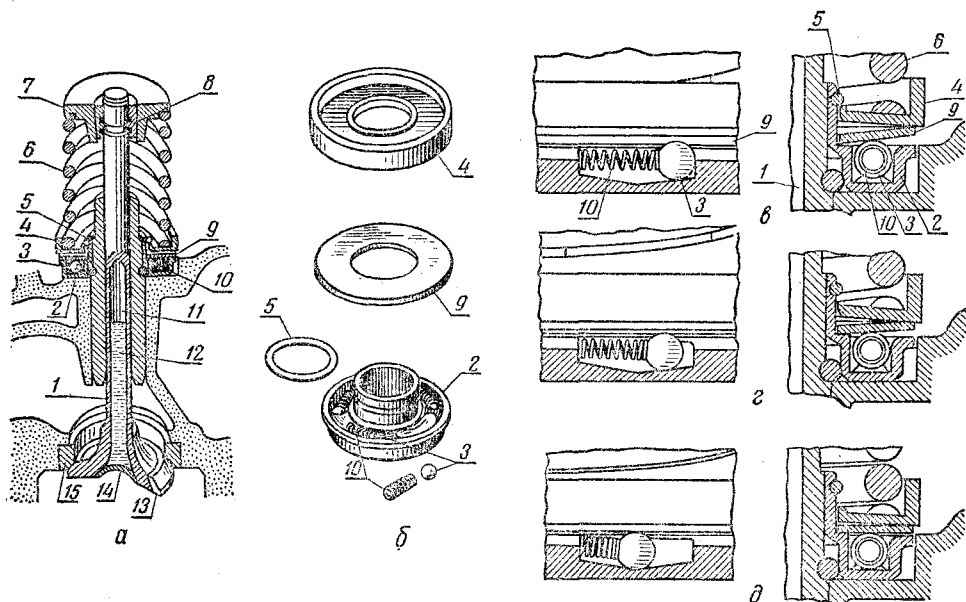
Выпускной клапан в сборе механизма газораспределения двигателя ЗИЛ-130 и схема поворота клапана:
